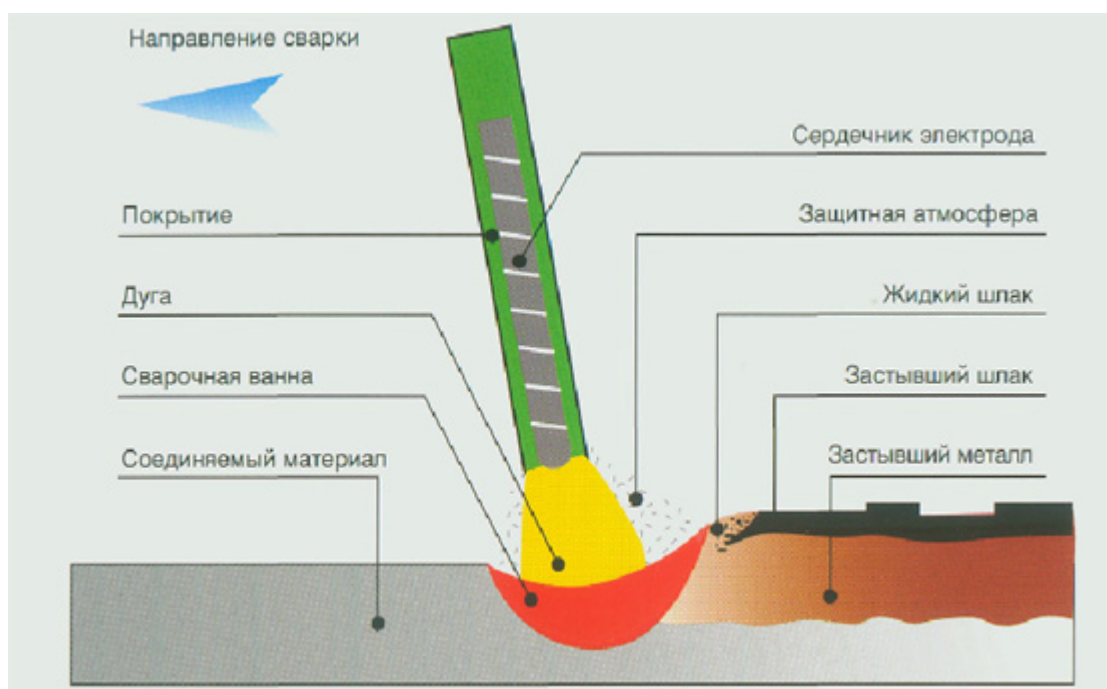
Схема ручной электродуговой сварки
